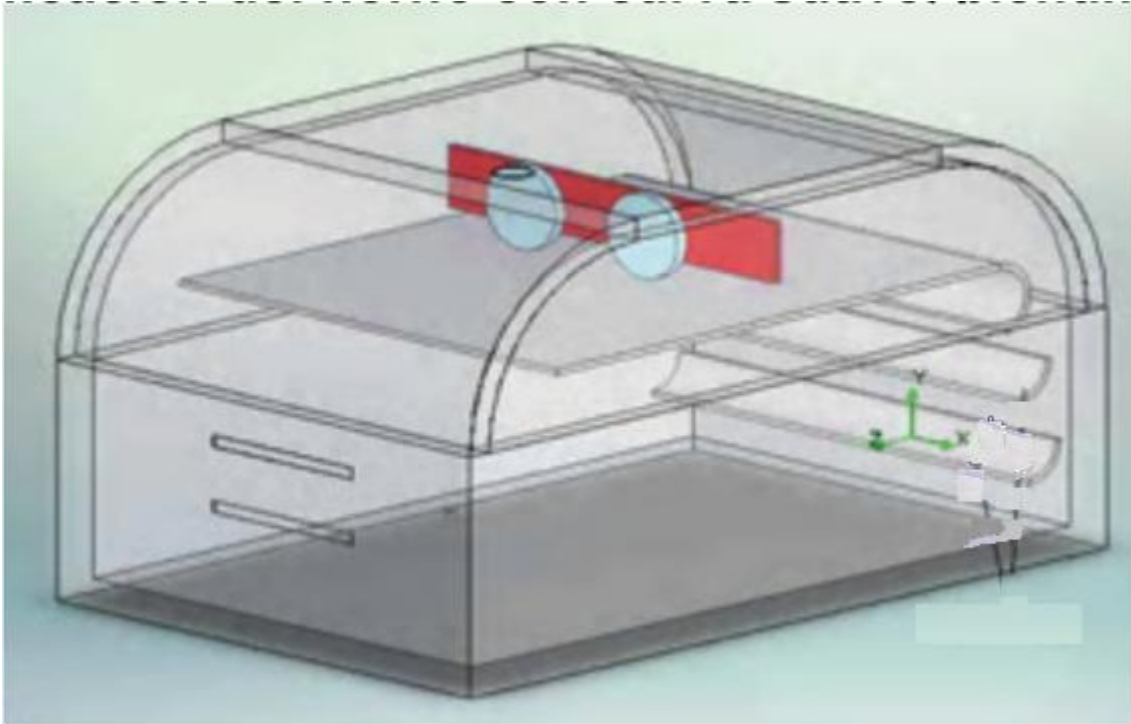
Disposición de ventiladores en la cámara de secado.
